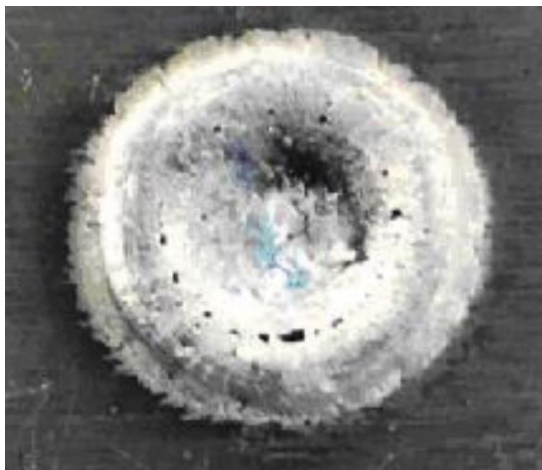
Зовнішній вигляд зварного з'єднання
